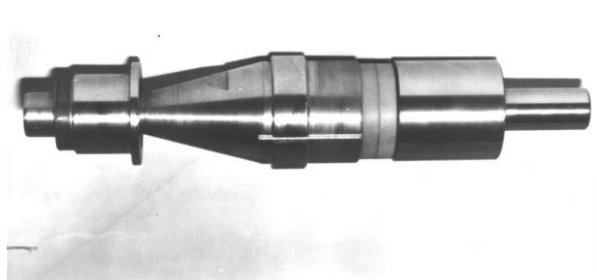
Вращающийся ультразвуковой шпиндель-преобразователь станков для обработки отверстий
